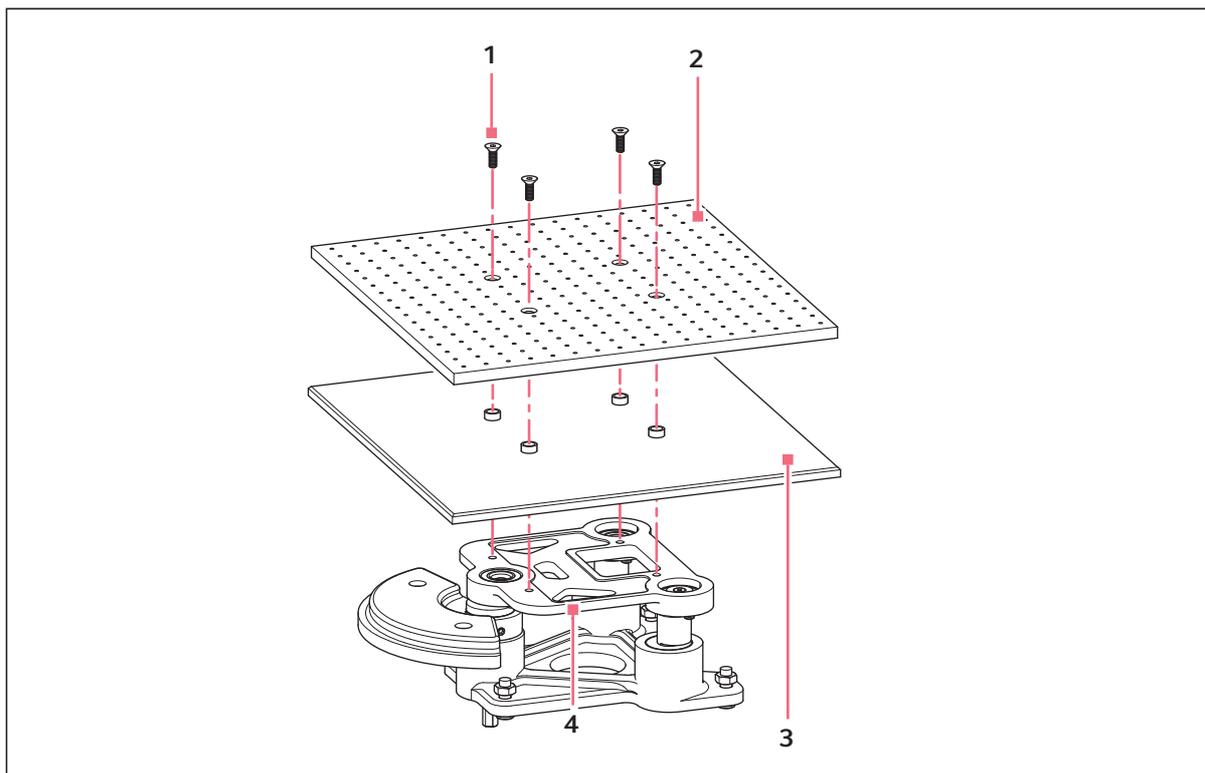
Installazione della piattaforma e della copertura di protezione dalle gocce
